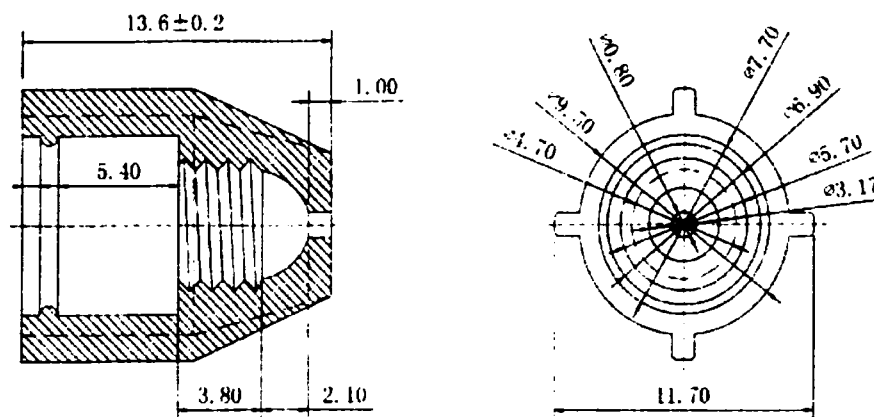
Схематичный чертеж колпачка торкера / Fig. 6 Structure of Torque cap
